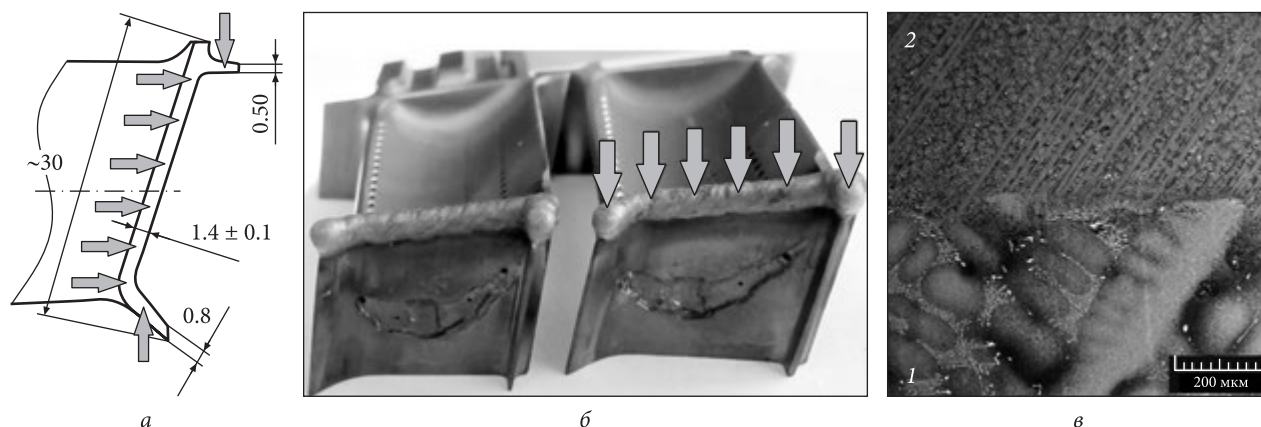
Ескіз зони ремонту (а), зовнішній вид (б) РЛ ТВТ авіаційного ГТД Д-18Т з наплавленими торцями бандажних полиць (місце наплавлення вказано стрілками) та типовий вигляд зварного з'єднання «основний (1) — наплавлений метал (2)» сплаву ЖС32-ВИ в зоні ремонту (в) за даними растрової електронної мікроскопії
